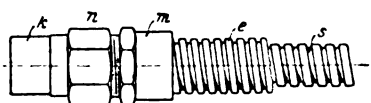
Aufgeschraubte Stopfbüchsenkupplung mit Innengewinde nebst Endschutzhülse.
